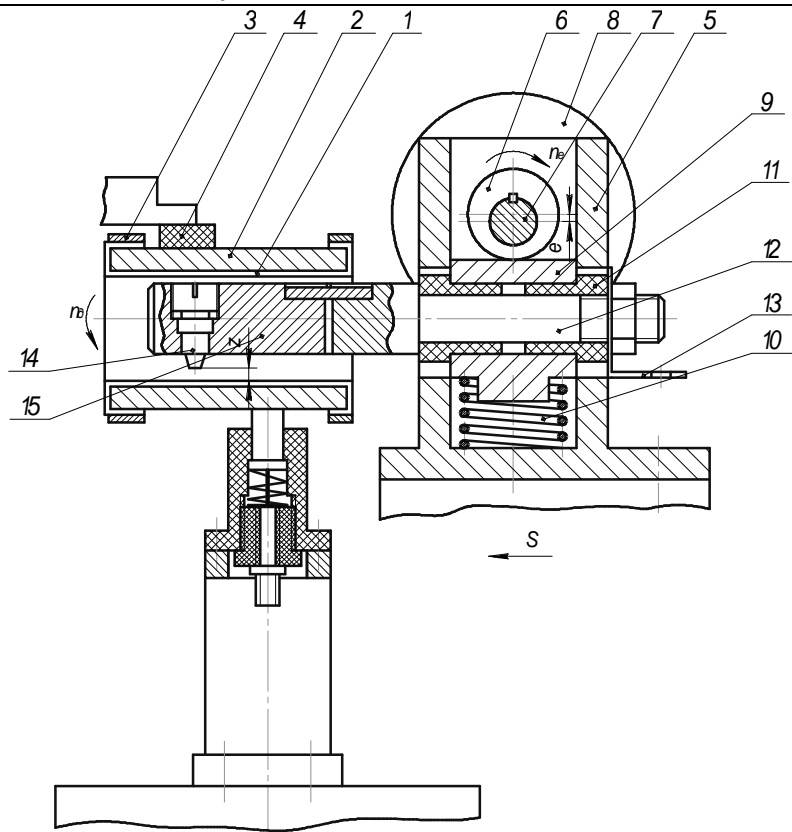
Установка деталі і пристрій з пружною штангою для електроконтактної дискретної цементації внутрішньої поверхні
